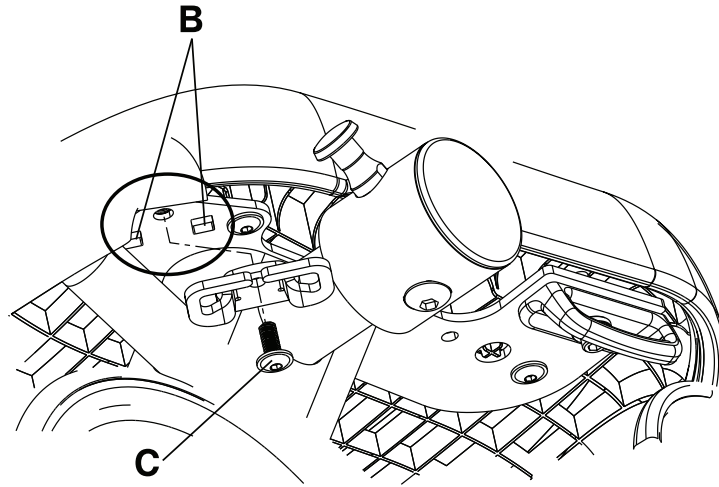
Montaggio della staffa per il fissaggio della cintura
